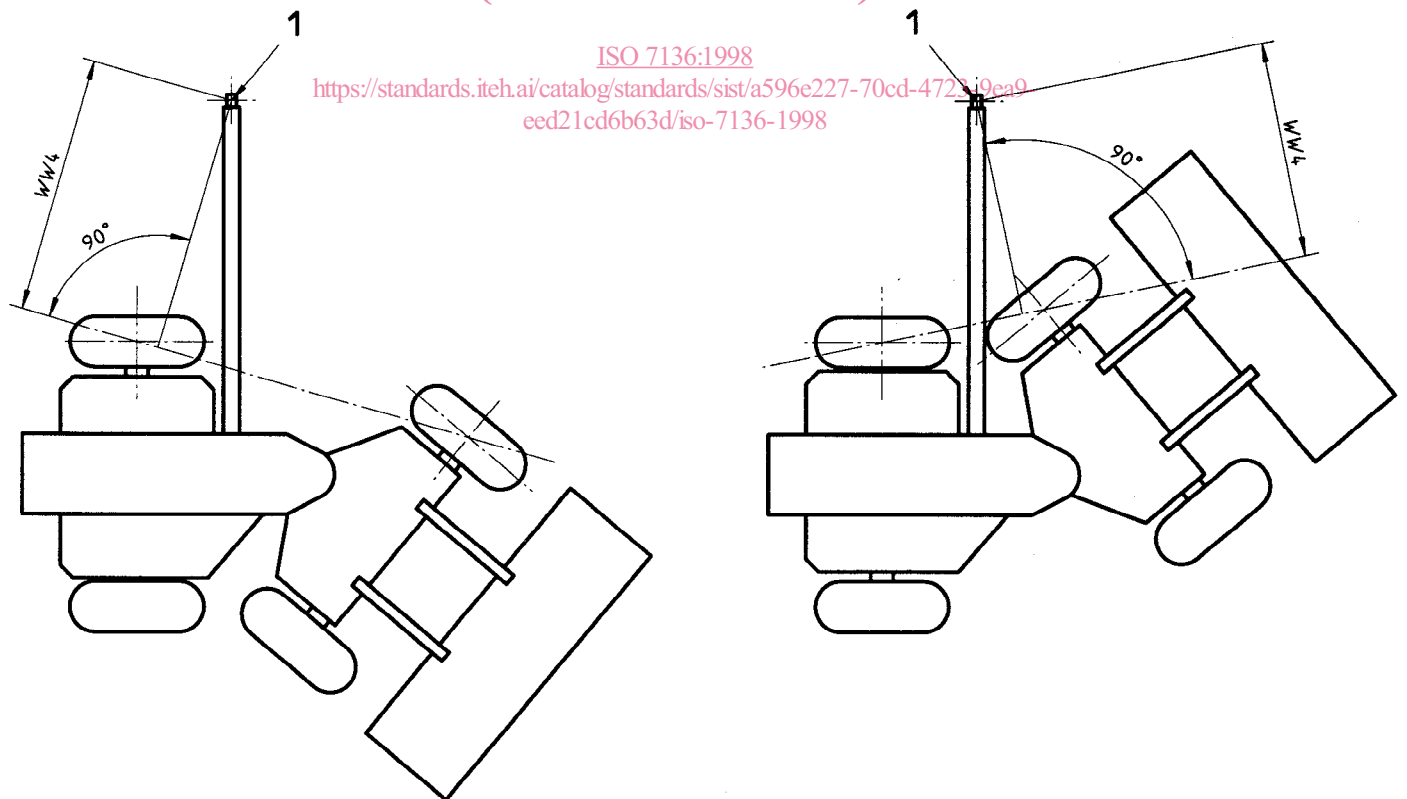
Dimension $WW4$ pour un engin à chenilles
